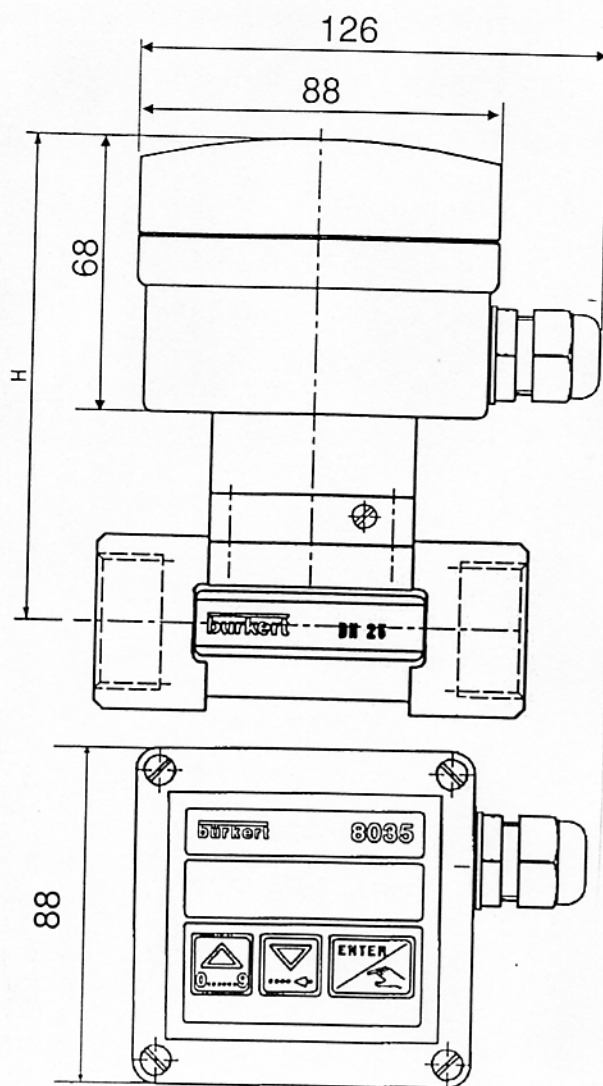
Dimensioni esterne del corpo elettronico SE35.
